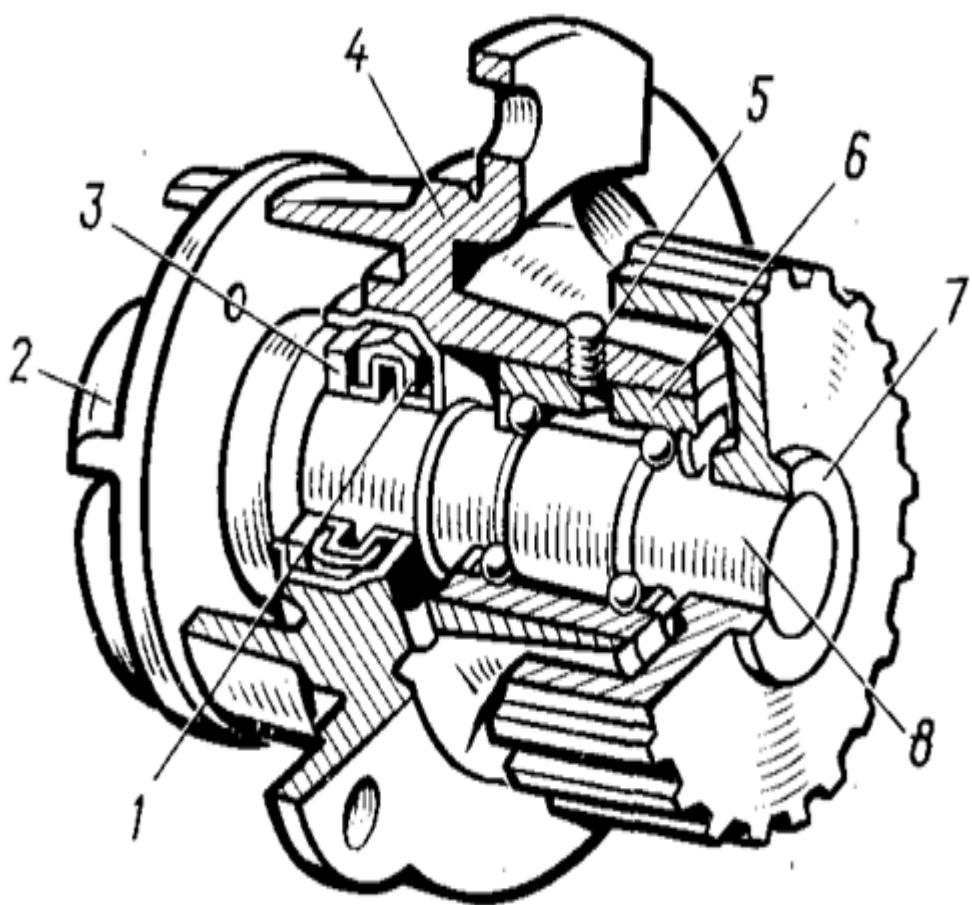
Насос охлаждающей жидкости в разрезе: 1 – уплотнительная манжета; 2 – крыльчатка; 3 – упорное кольцо манжеты; 4 – корпус; 5 – стопорный винт подшипника; 6 – шариковый подшипник; 7 – приводной зубчатый шкив; 8 – вал насоса
